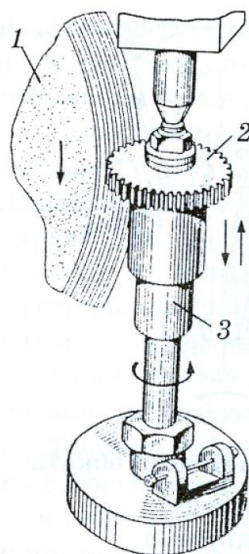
Шлифование зубьев цилиндрических колес червячным кругом: 1 – червячный шлифовальный круг; 2 – обрабатываемое зубчатое колесо; 3 – оправка
